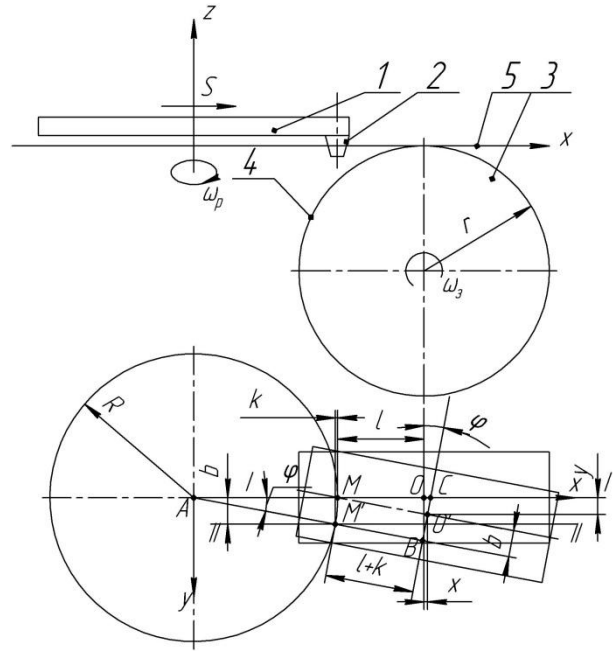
Схема формоутворення методом обкату зі зміщення заготовки
